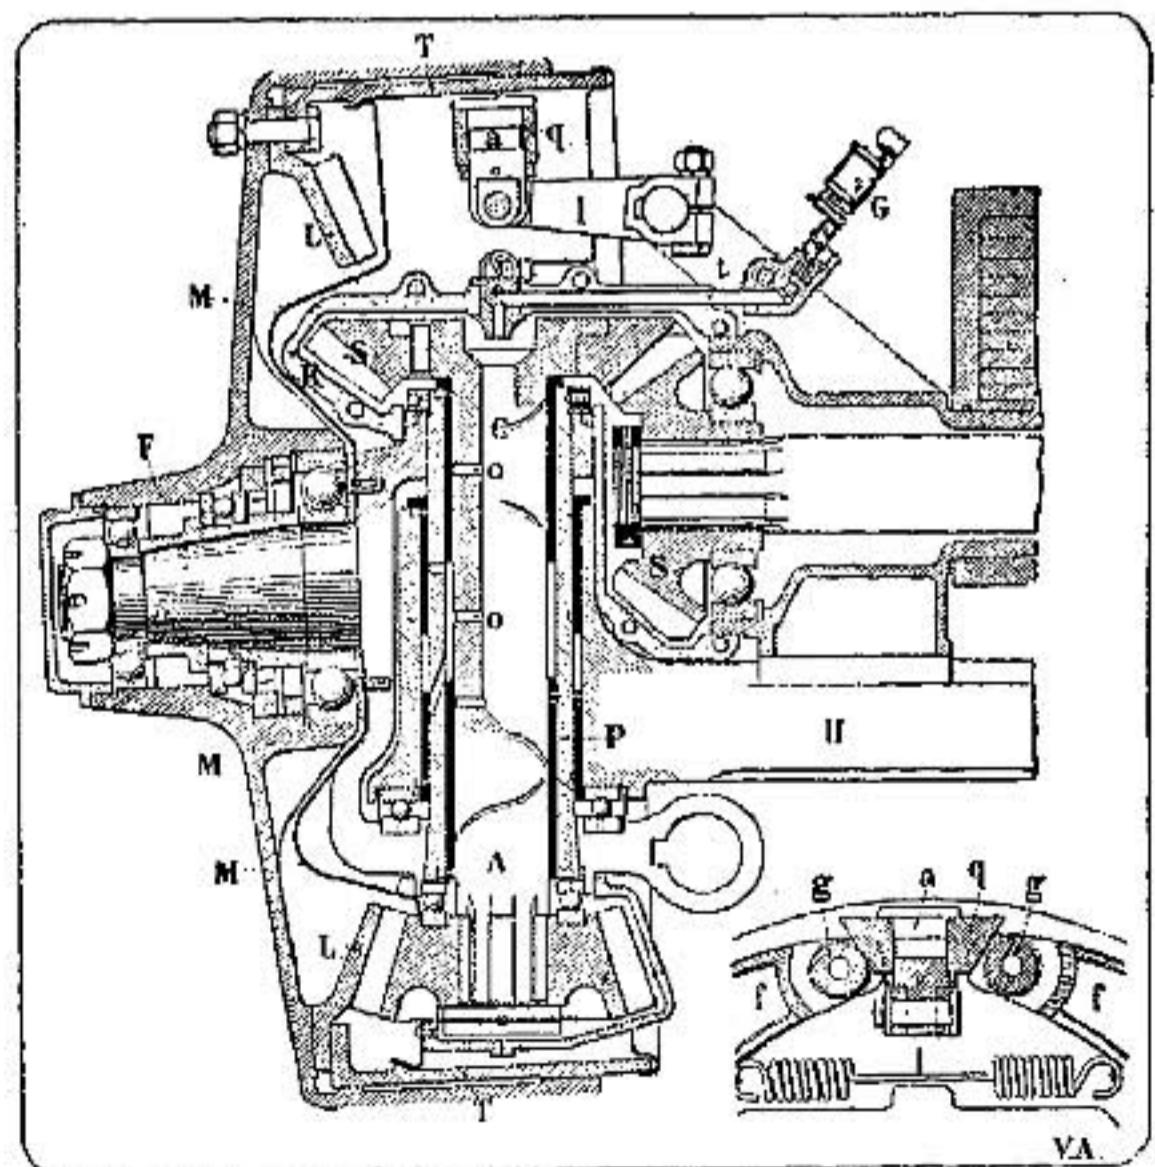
Конструкція направляющихъ и движущихъ колесъ трактора Панаръ и Левассоръ.
